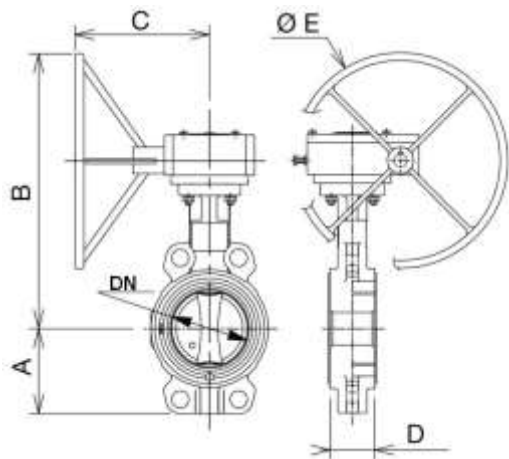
Габаритные и присоединительные размеры затворов дисковых поворотных модификации VFY-WG с центрирующими проушинами
